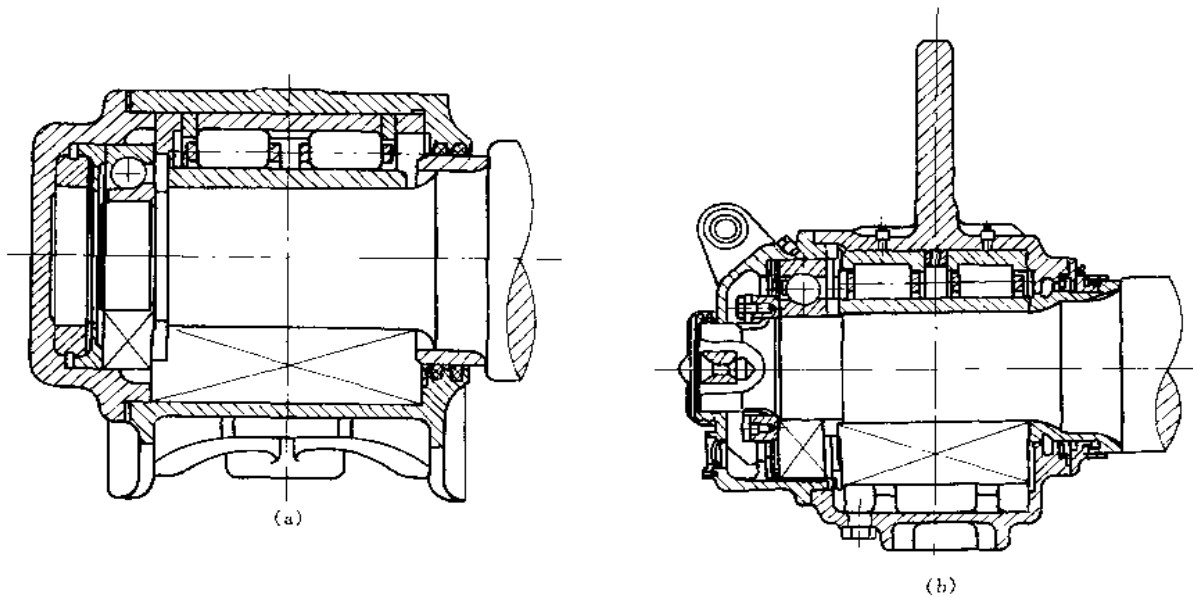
用圆柱滚子轴承做轴箱轴承
